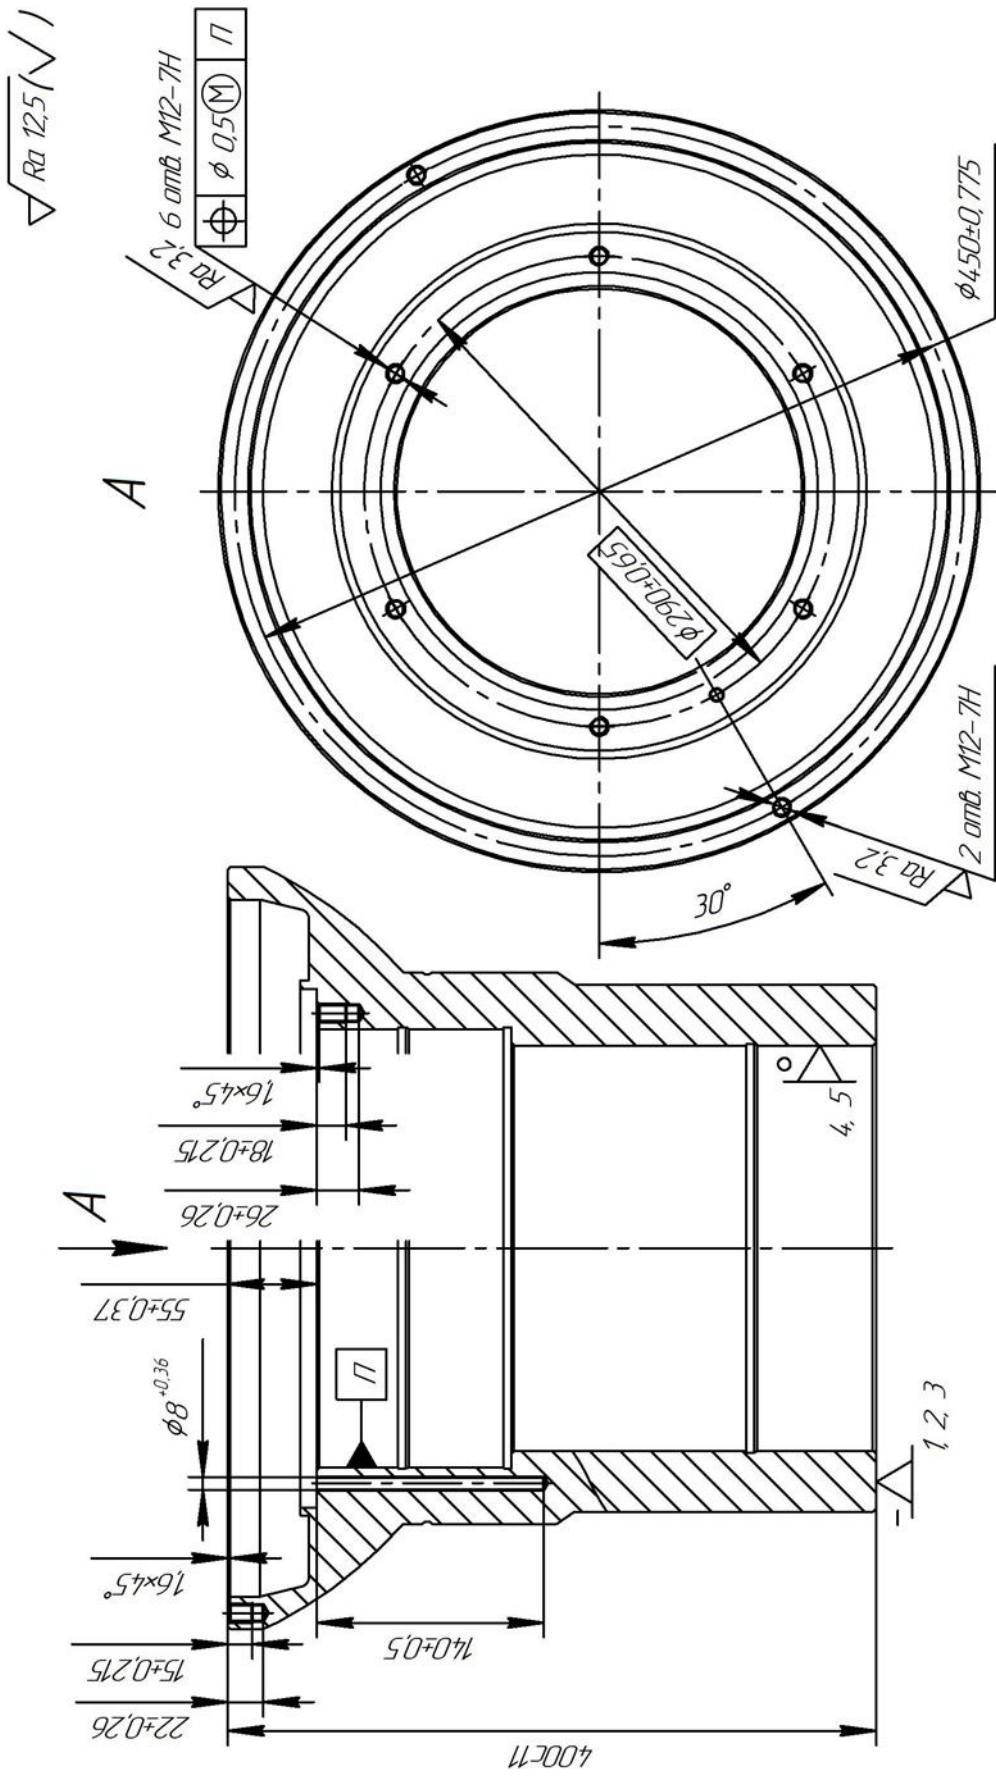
Альтернативна схема базування заготовки на операції радіально-свердильній 050 (установ А)
